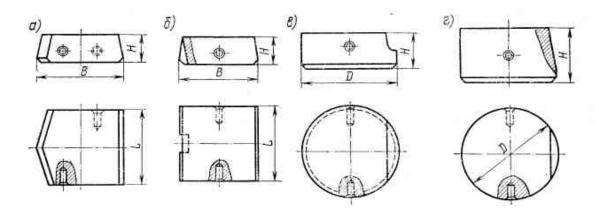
Схемы молотовых вставок с клиновым креплением: а – угловая призматическая; б – прямоугольная призматическая; в – цилиндрическая для крепления призматическим клином; г – цилиндрическая для крепления цилиндрическим клином
